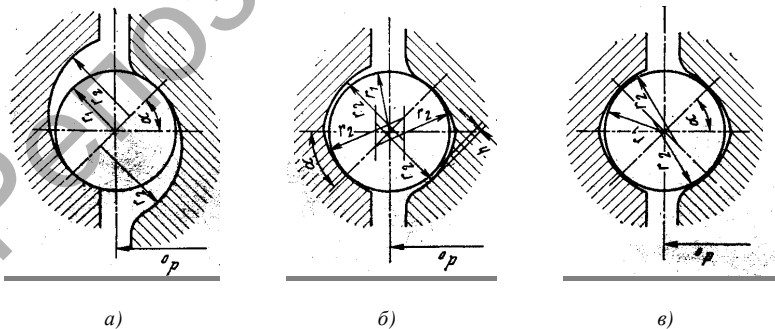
Профили резьбы винта и гайки шариковых винтовых пар
